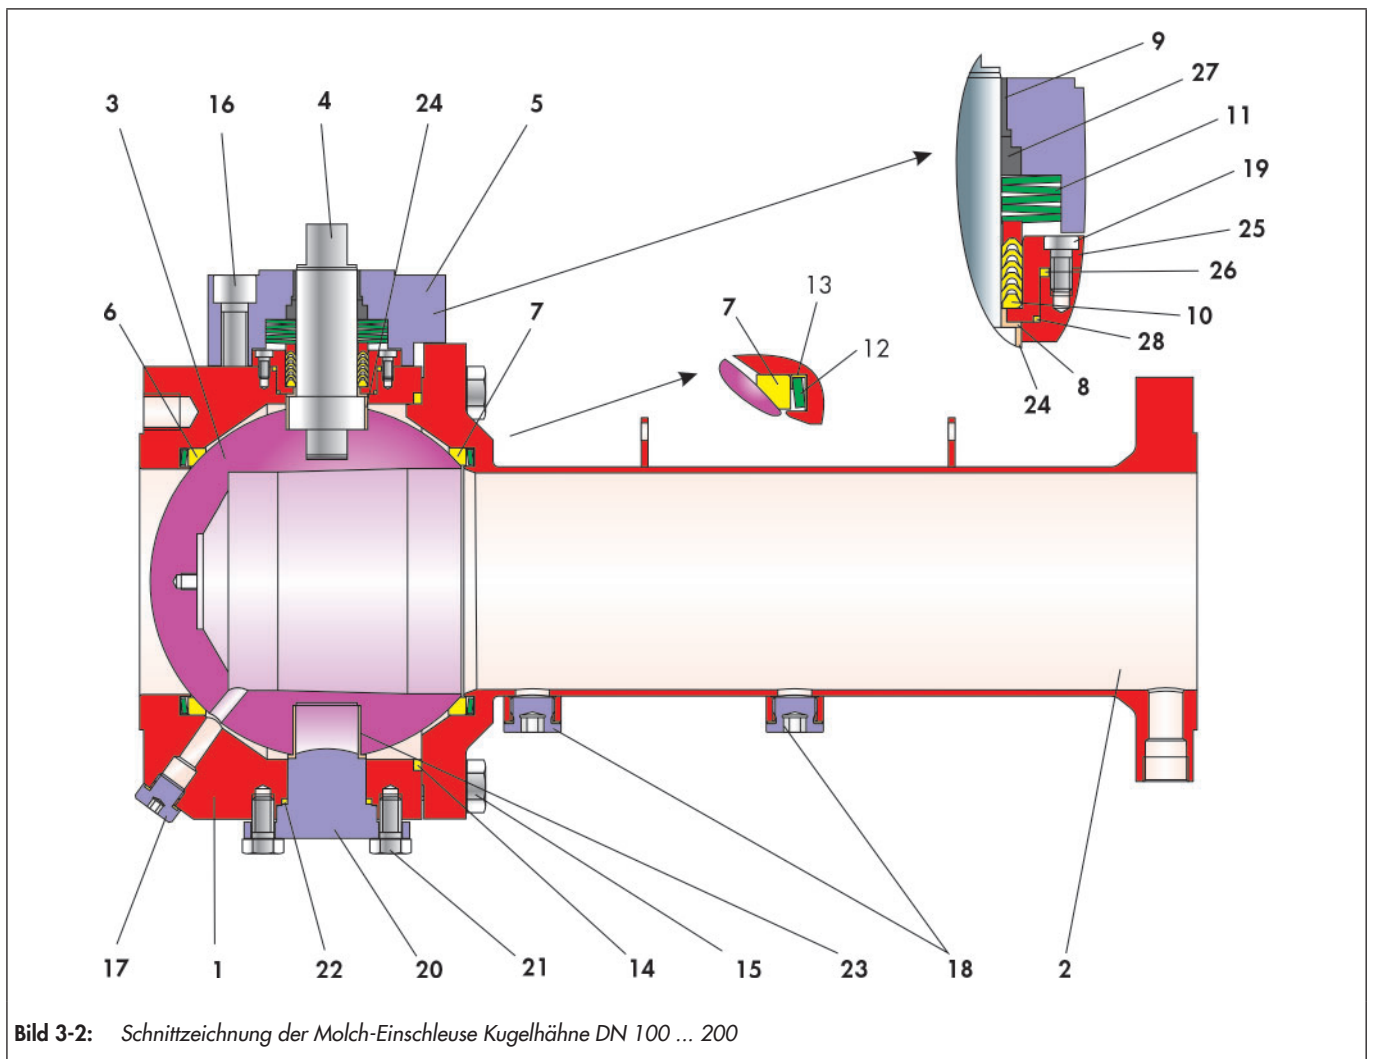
Schnittzeichnung der Molch-Einschleuse Kugelhähne DN 100 ... 200
